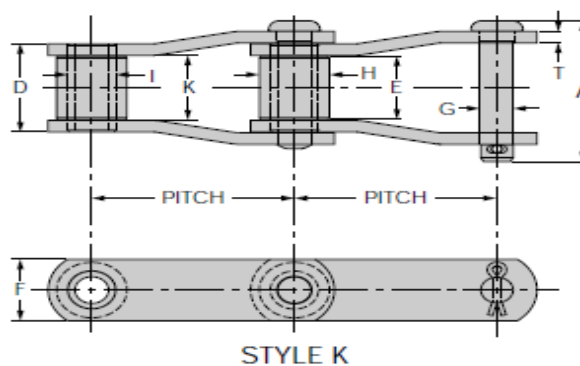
Esquema de cadena tipo K para las bandas de placas metálicas ^[53]
